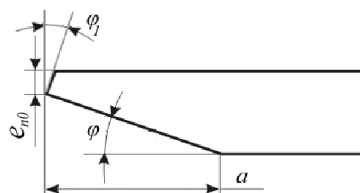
Профіль різця для обробки опуклої сторони зуба
